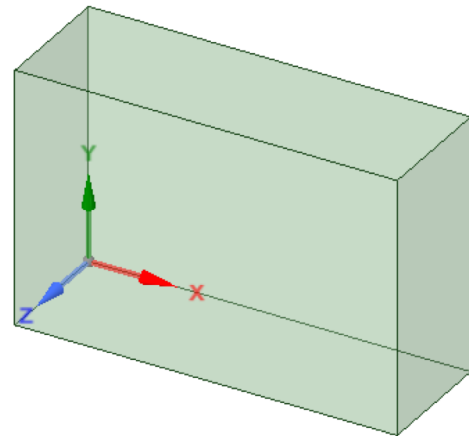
B Posizionamento sul piano XY con base sul piano YZ.
